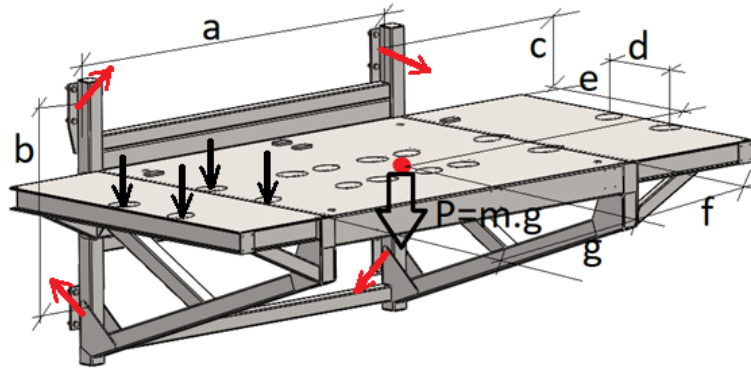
Estrutura da cesta da plataforma elevatória; DCL do movimento horizontal, saída da carga
